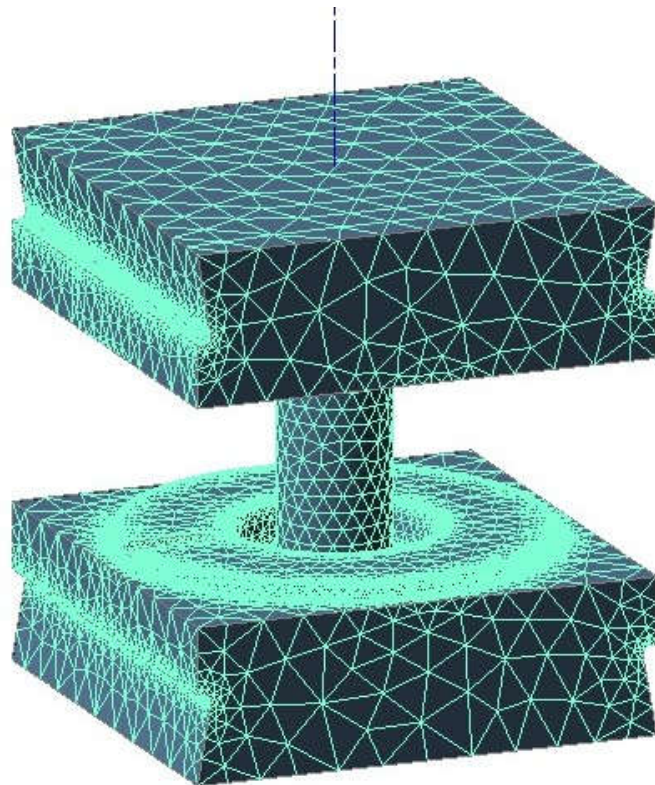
Позиціоновані моделі штампового оснащення та заготовки після розбиття сітки скінчених елементів
